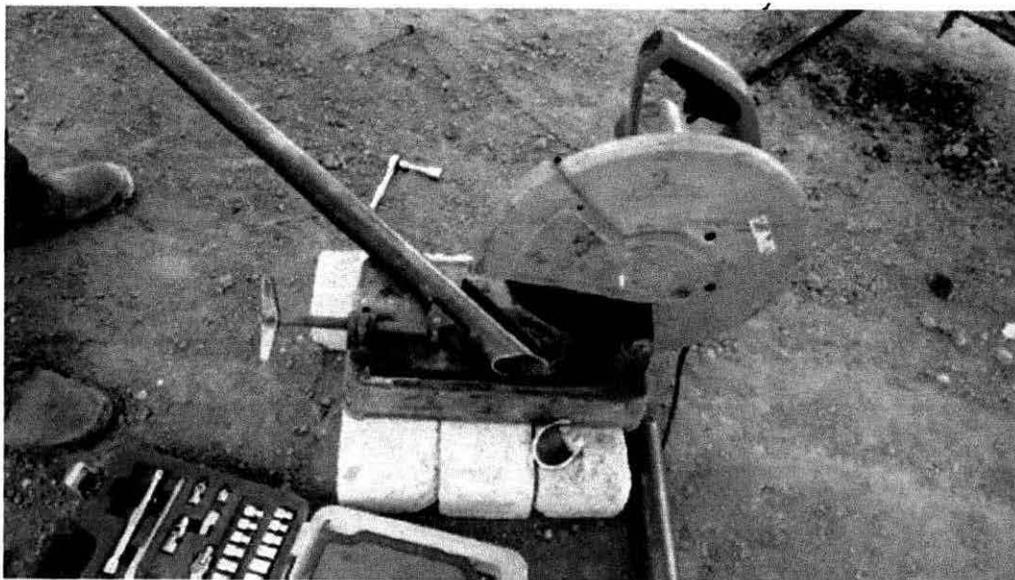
Corte 45 previo a la instalación de tubo en tanque
